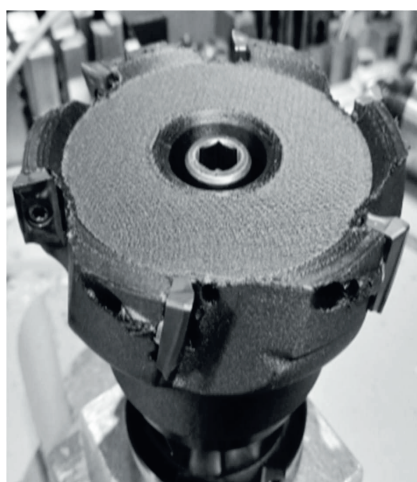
Корпус фрезы из материала Опух, изготовленный с применением аддитивных технологий
